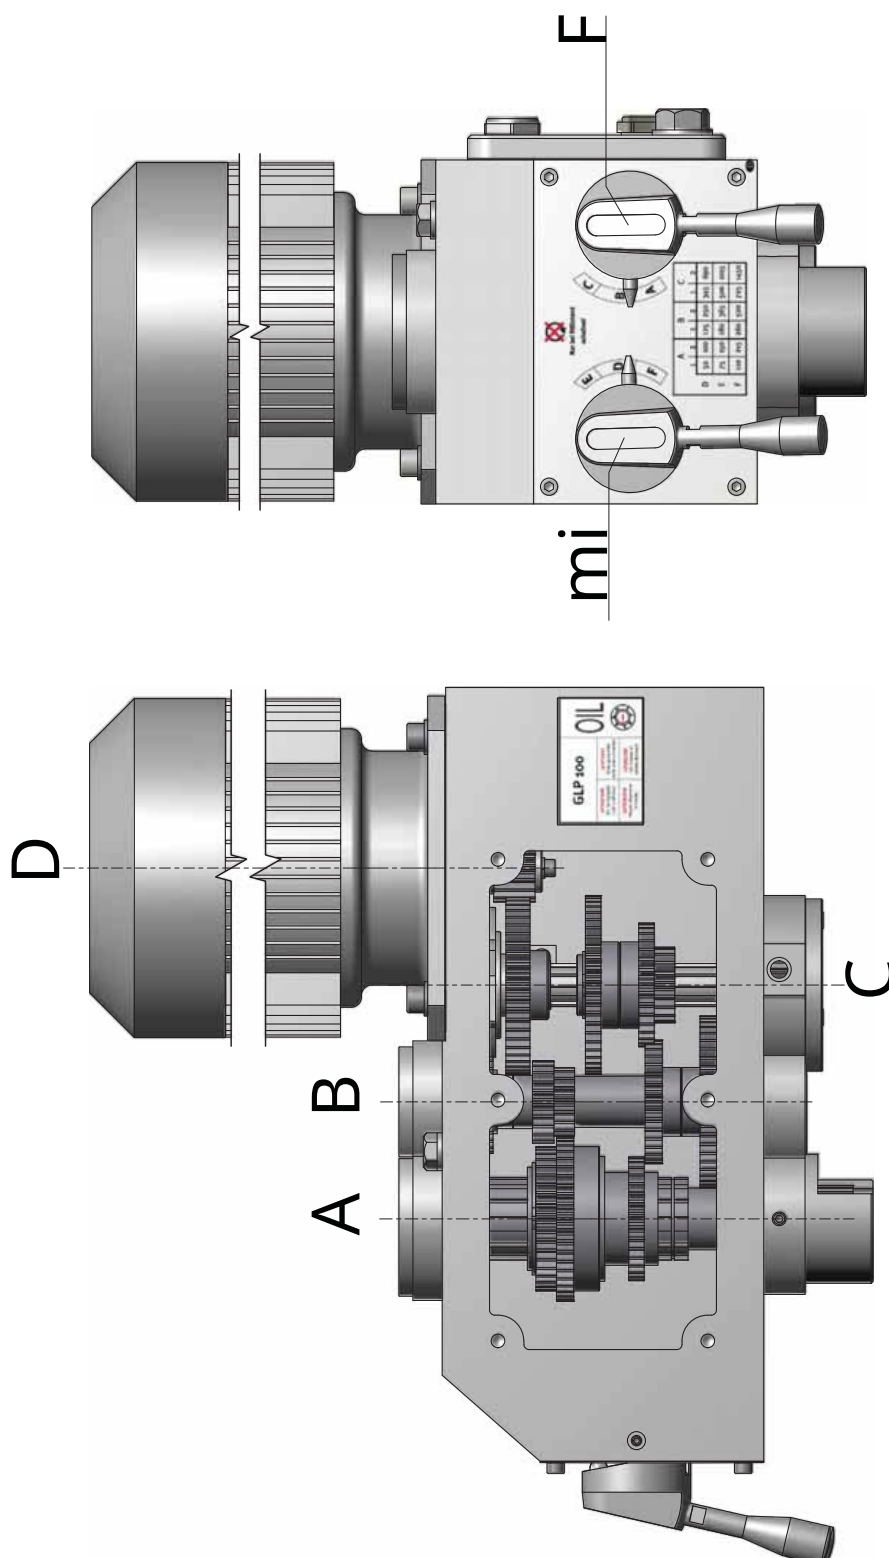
Getriebe Bohrspindel - Husillo principal de la caja de cambios
